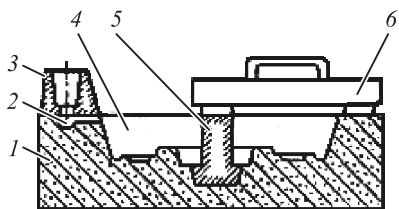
Устройство формы с размещением отливки в нижней открытой опоке: 1 – нижняя полуформа; 2 – питатель; 3 – литниковая чаша; 4 – полость формы; 5 – стержень; 6 – груз
